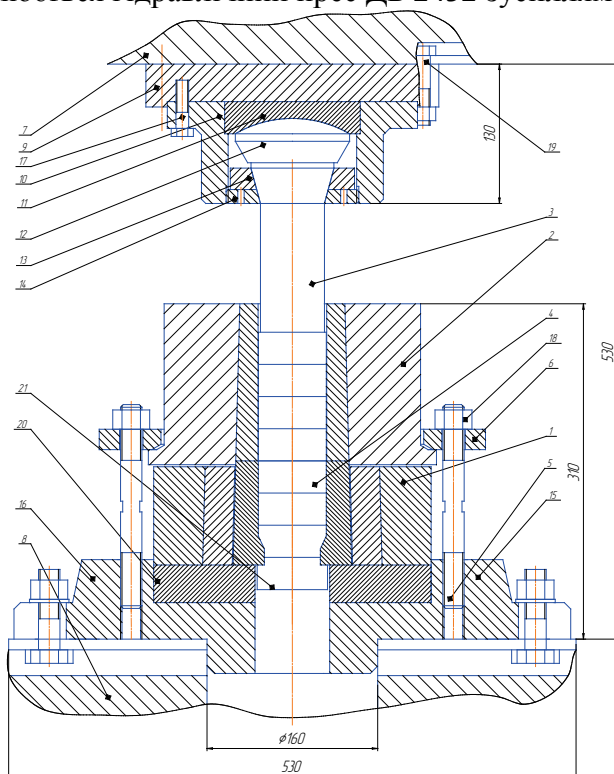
Загальний вигляд штамп для прямого видавлювання зубчастого профілю з роздачею
